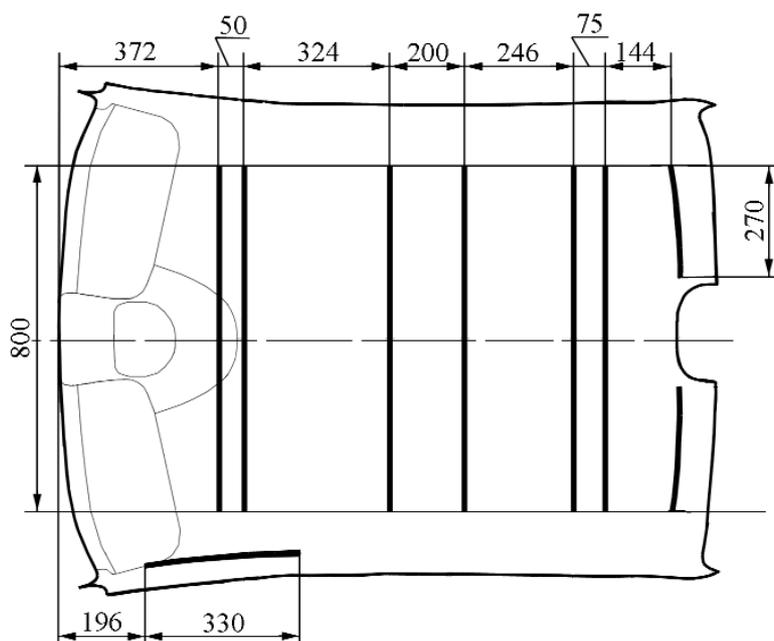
Схема нанесения валиков клея на обивку крыши.
